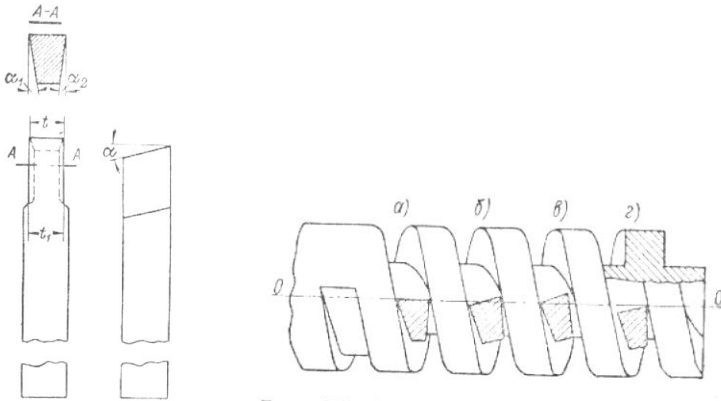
Резец для нарезания прямоугольной резьбы и способ установки резца для её формирования
